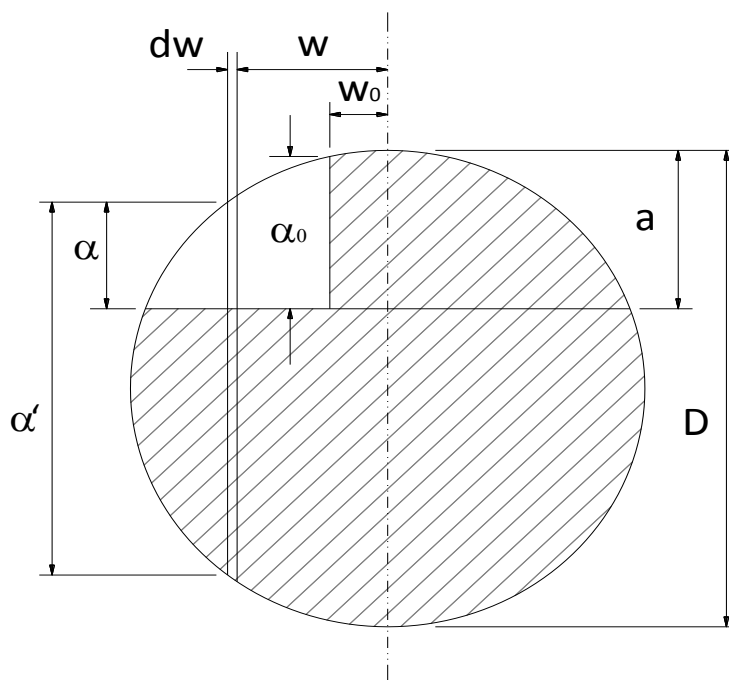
Sección transversal del eje en la localización de la fisura.
